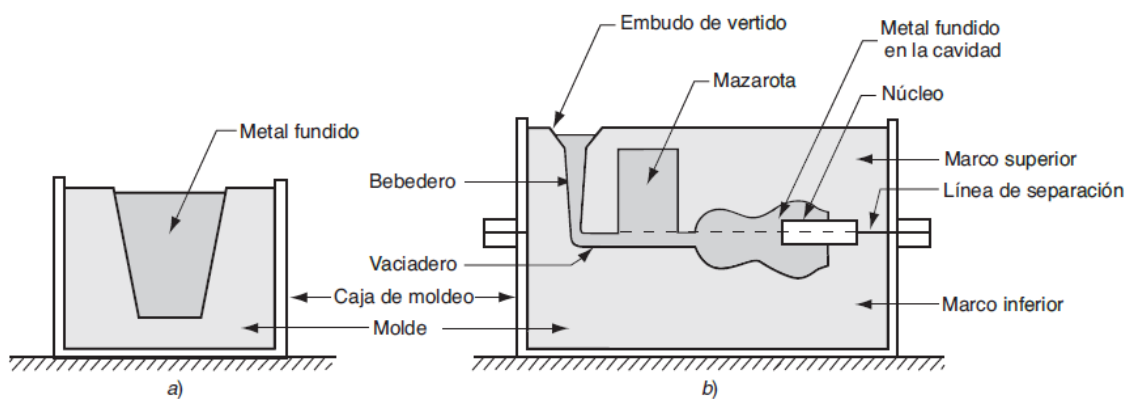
Tipos de molde por su forma. a) Molde abierto, b) Molde cerrado. [3]
